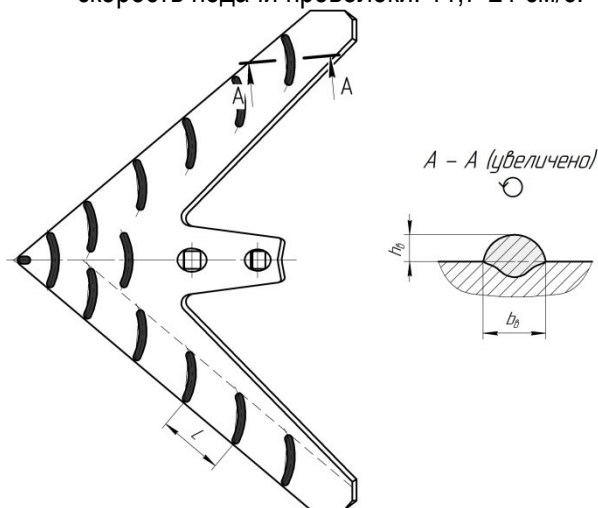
Схема расположения наплавляемых на рабочую поверхность стрелчатой лапы валиков:
